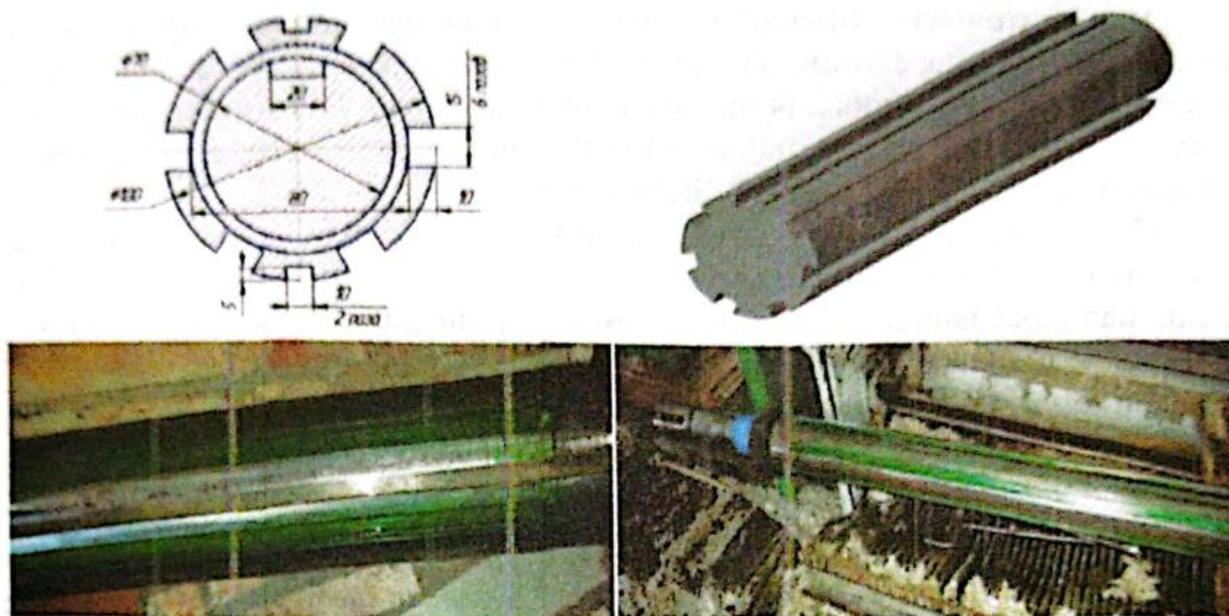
Конструкция продольной канавки на поверхности вала пильного цилиндра
